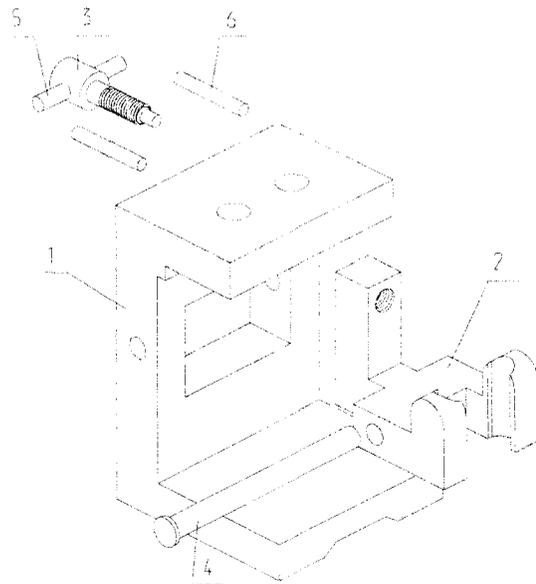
Состав сборочной единицы: 1 - корпус, 2 - рычаг, 3 - винт, 4 - ось, 5 - ручка, 6 - штифт
